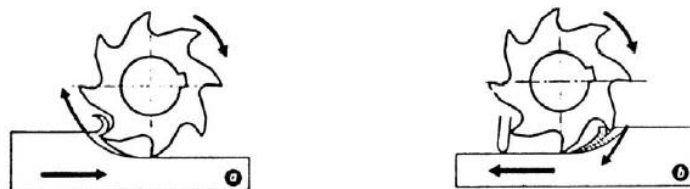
Fresagem cilíndrica: a) fresagem a empurrar; b) fresagem a puxar [23].
